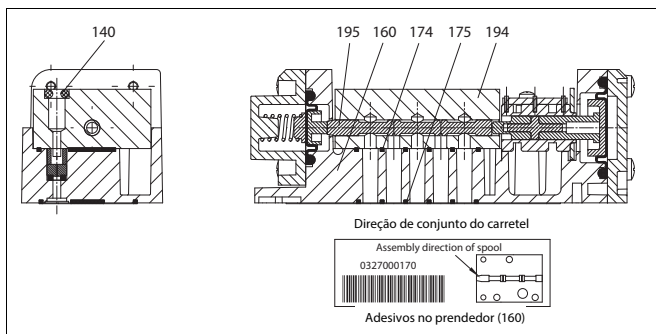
Conjunto da válvula de carretel, ND9100 e ND7100
